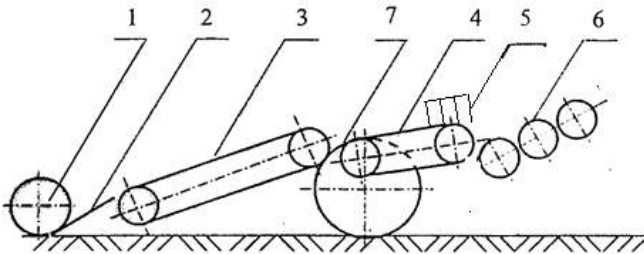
Конструктивна схема картоплекопача зі спіральним очисником: 1 – коток; 2 – викопувальні робочі органи; 3, 4 – пруткові просіювальні елеватори; 5 – звужувальні решітки; 6 – спіральний очисник; 7 – опорні колеса
